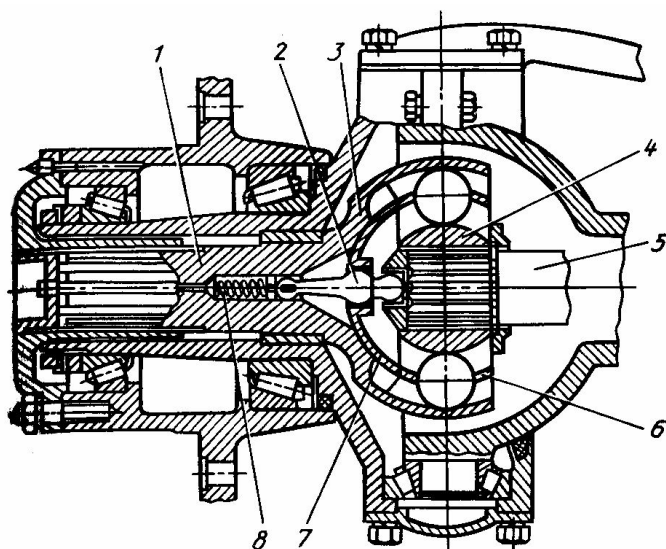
Шестишариковый карданный шарнир с делительным рычажком (типа «Рцепп») 1, 5 – вал; 2 – делительный рычажок; 3 – сферическая чашка; 4 – кулак; 6 – сепаратор; 7 – направляющая чашка; 8 – пружина.
